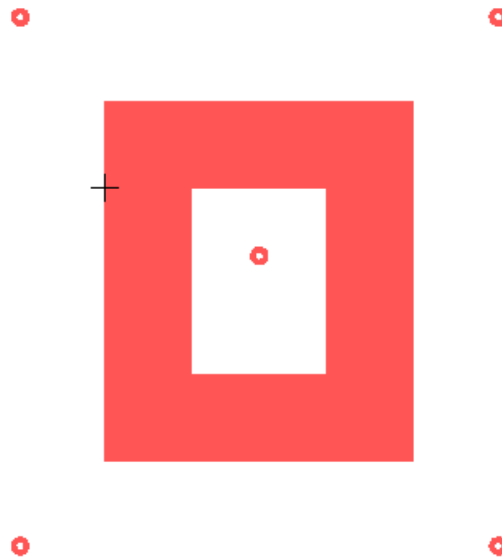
Masque 2 de l'électrode mobile (la plaque supérieure de PCB)
